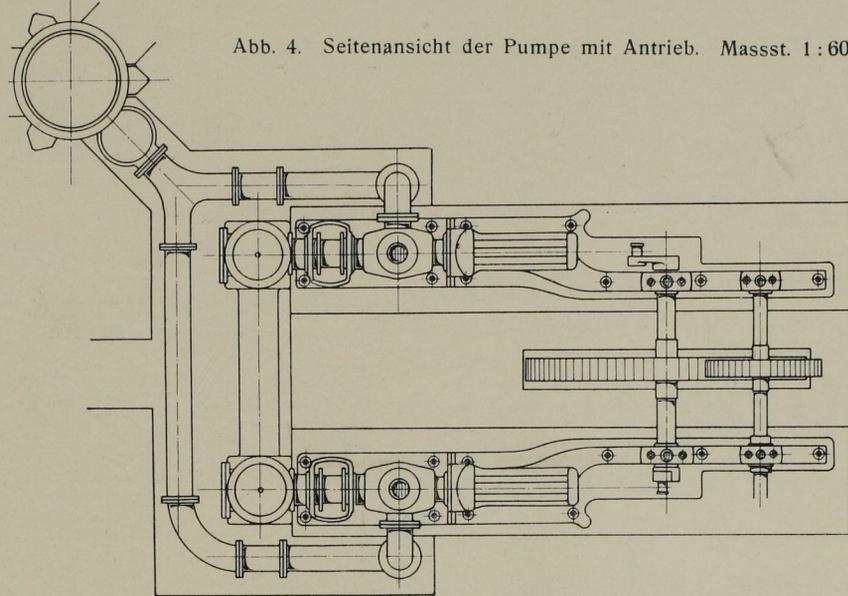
Grundriss der Pumpe mit Antrieb. Masst. 1:60.
